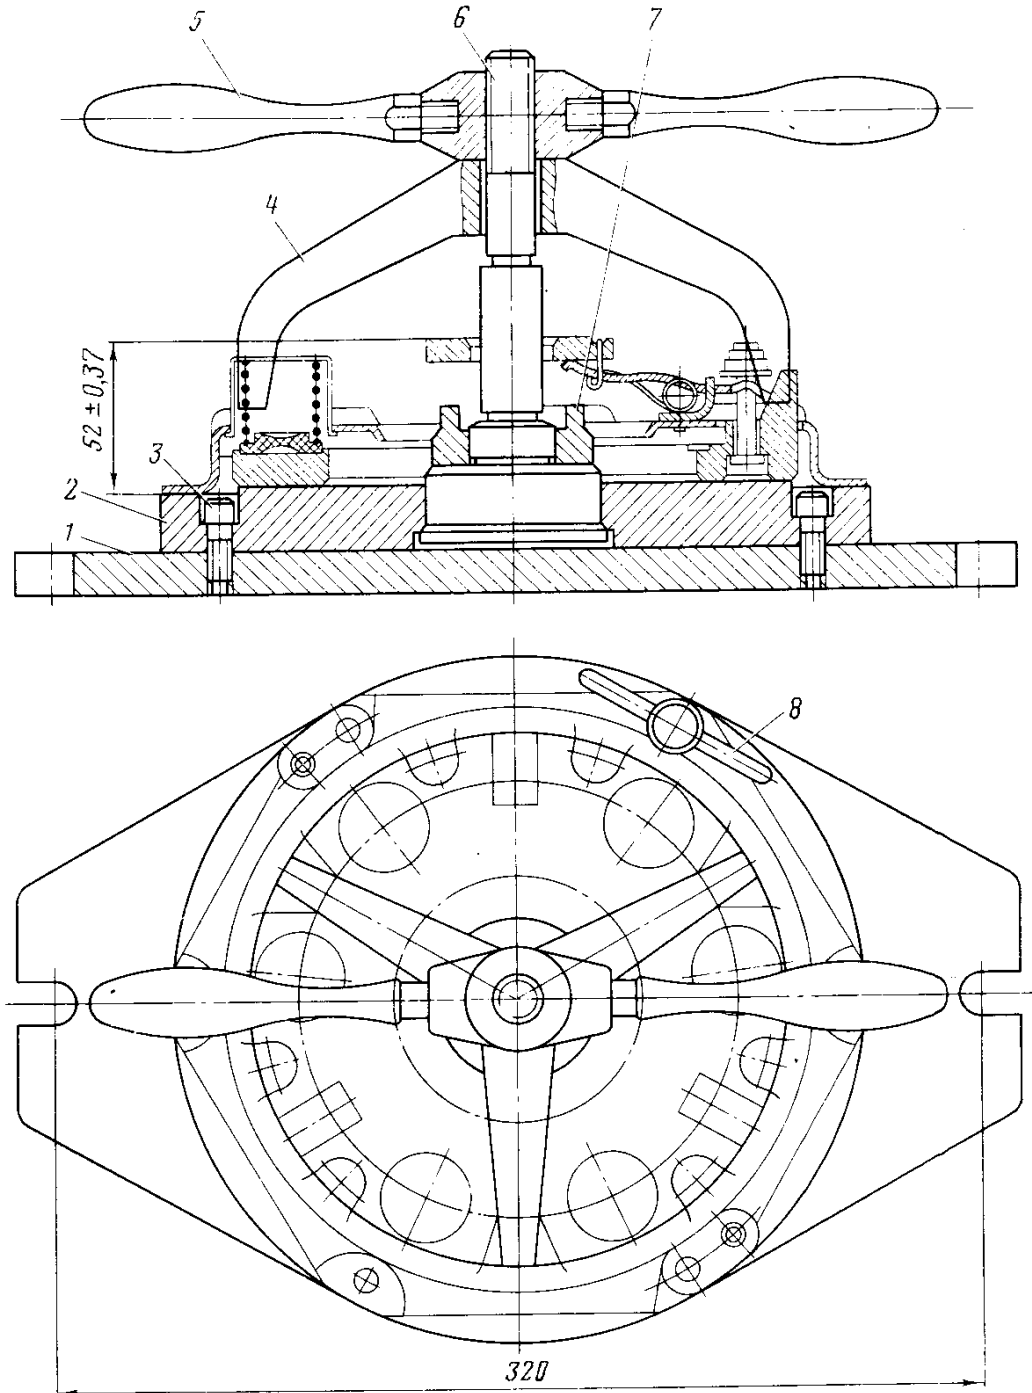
Приспособление для разборки и сборки сцепления: 1 — плита; 2 — опора; 3, 6 — винты; 4 — прижимной кронштейн; 5 — рукоятка зажима; 7 — упор; 8 — винт зажима
